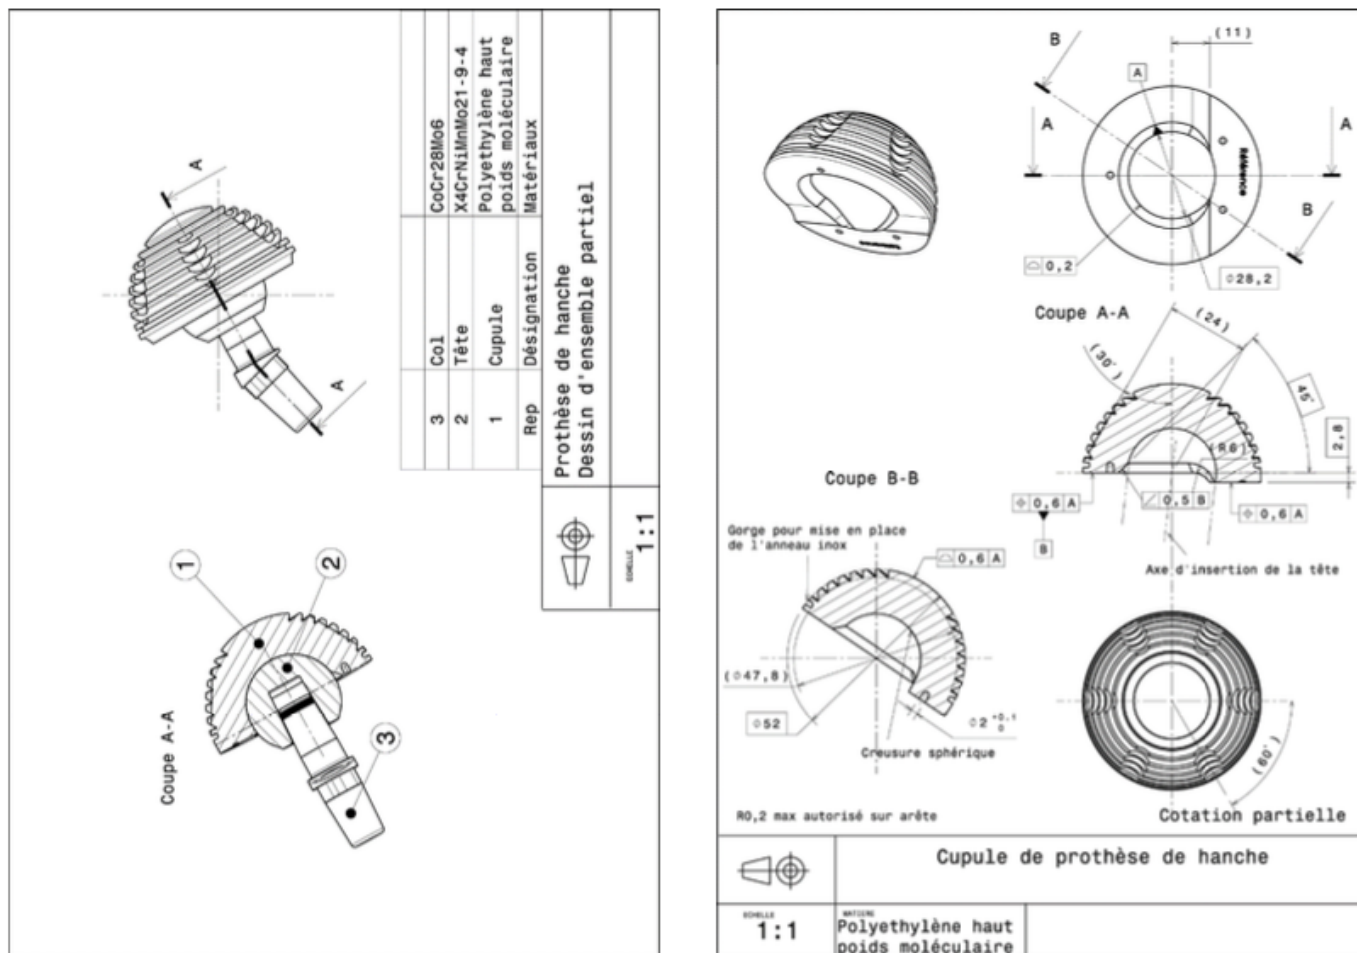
Dessin d'ensemble (à gauche) ; dessin de définition d'une pièce (à droite)
